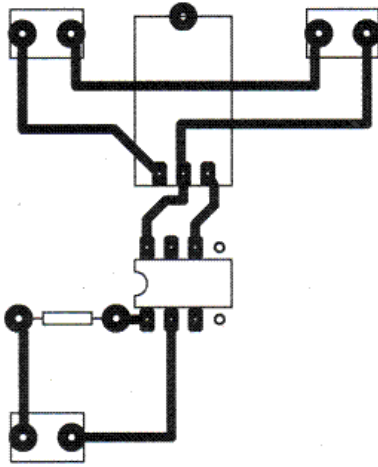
BEC Motor Sürücü Devresi Malzeme Yerleşim Planı
